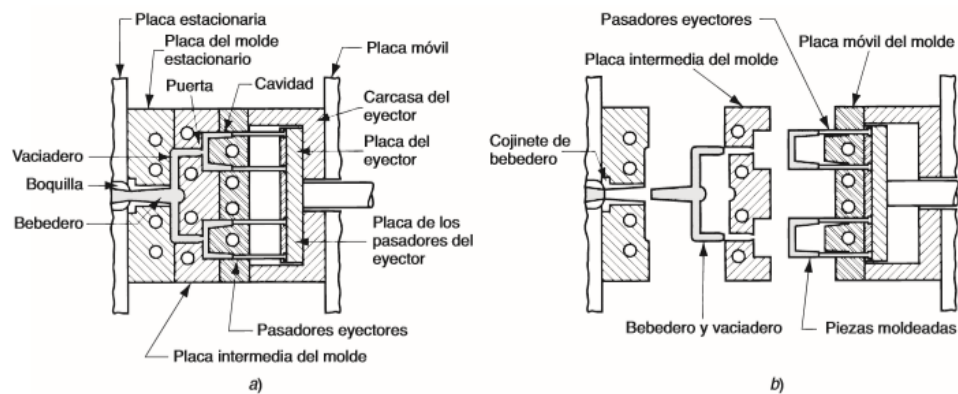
6 Molde de tres placas: a) cerrado y b) abierto
